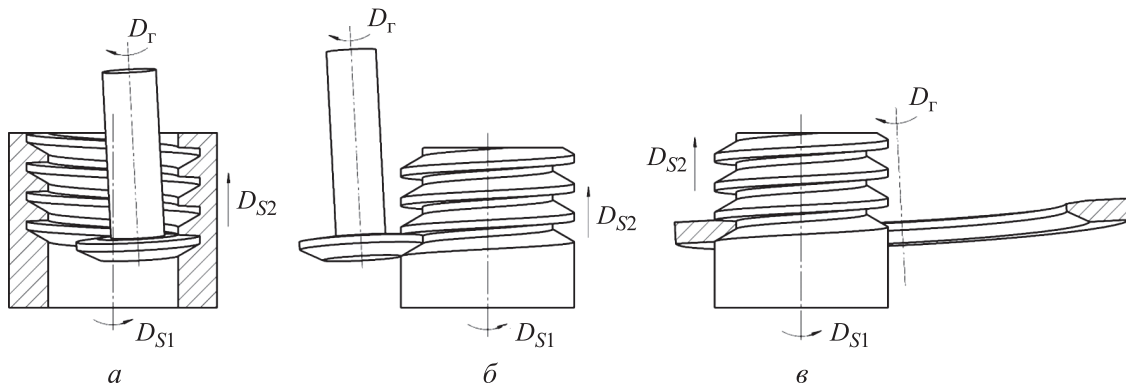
Кинематические схемы формообразования резьб однодисковой ФОП по схеме со скрещивающимися осями инструмента и УР:
